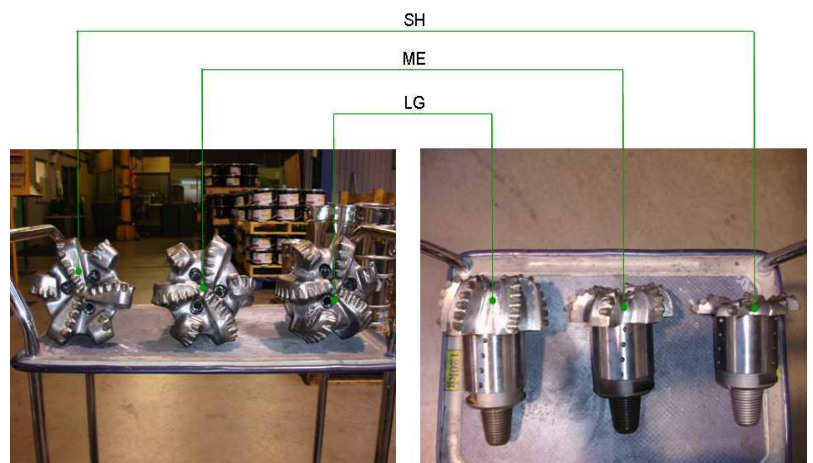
Photo des 3 profils de coupe : Short (SH), Medium (ME) et Long (LG)
